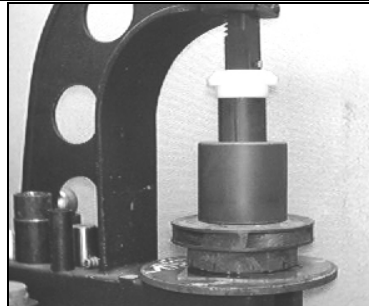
Inserte el Bujes Principal dentro del impulsor usando la herramienta PT0438.
